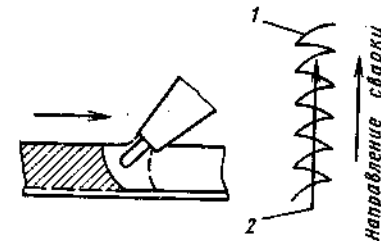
Движения горелки и проволоки при правой сварке с разделкой кромок:
